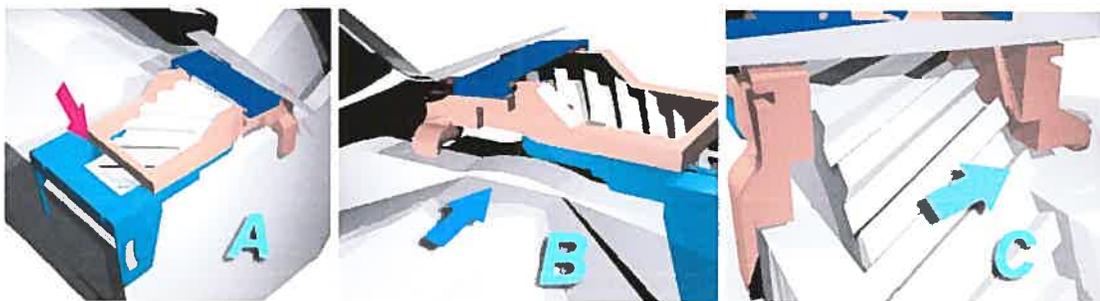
Problèmes de design du deuxième prototype.¹⁵⁷
